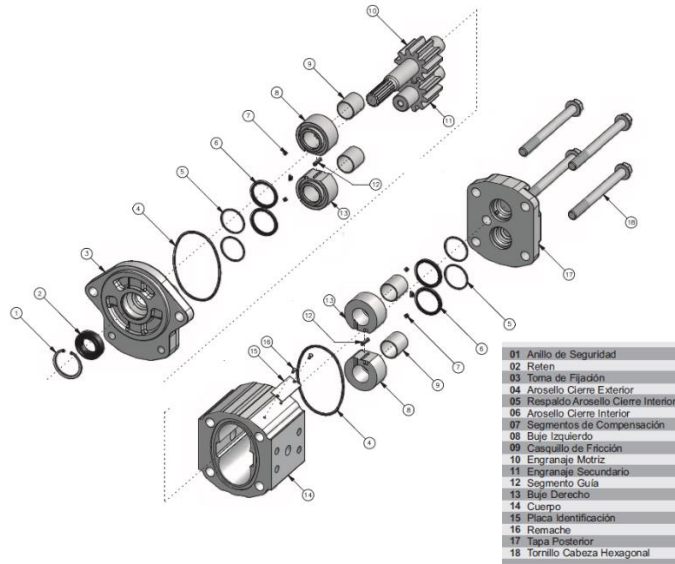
Vista explosionada bomba hidráulica de engranajes de volumen constante
